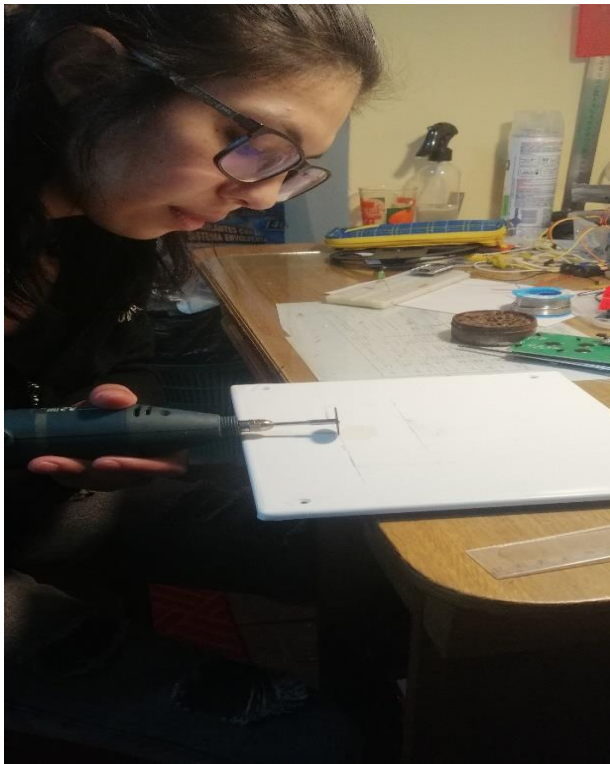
Corte de la caja para la adaptación de los componentes y cables
